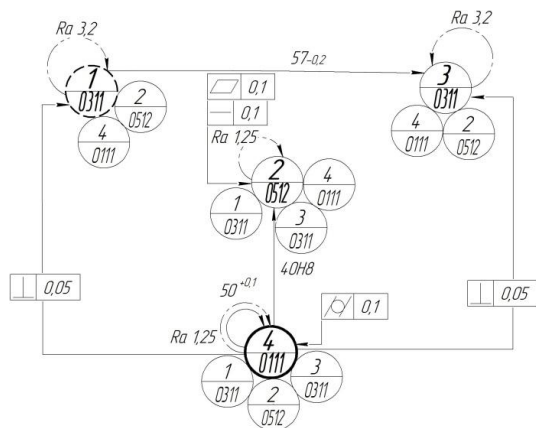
Граф размерных связей между элементарными поверхностями детали «Валик», насыщенный информацией о конструкторских базах детали
